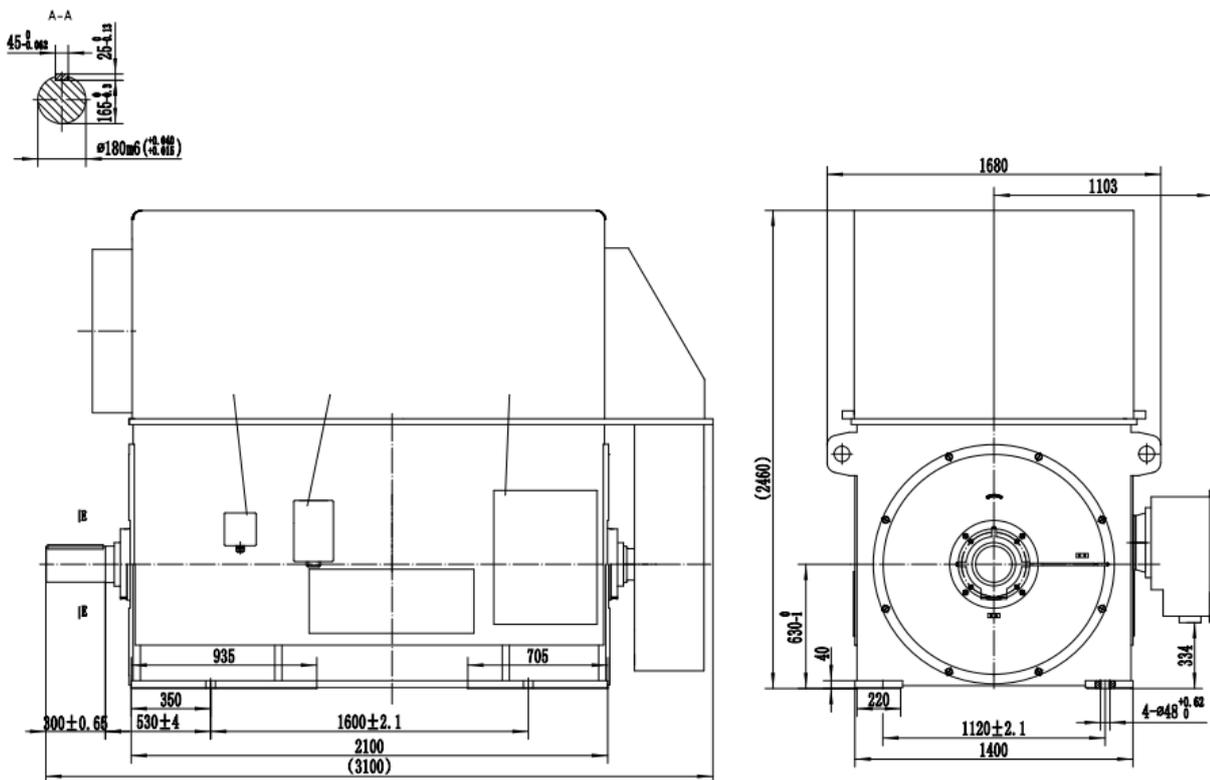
Асинхронные двигатели серии А4-500 6 кВ (3 кВ). Габаритные, установочные и присоединительные размеры
